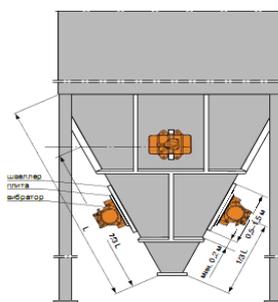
Схема возможной установки вибратора на промышленный бункер
